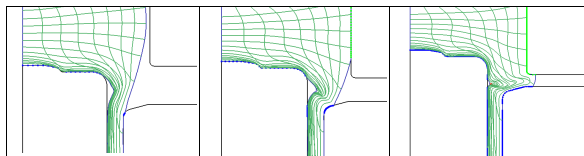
Область образования дефекта заготовки «складка металла»
